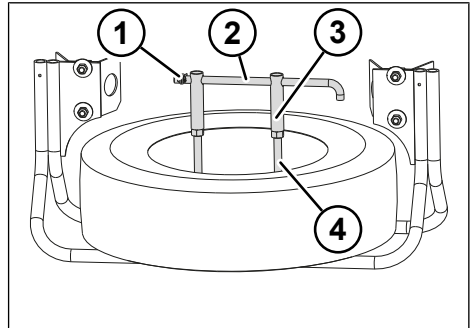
Держатель запасного колеса для сдвоенных шин и шин автомобиля
